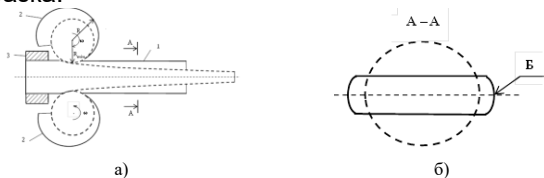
Схематичне зображення процесу вальцювання на а); А-переріз деформованої заготовки; б) Б-поверхня контролю за деформаціями й руйнуванням
